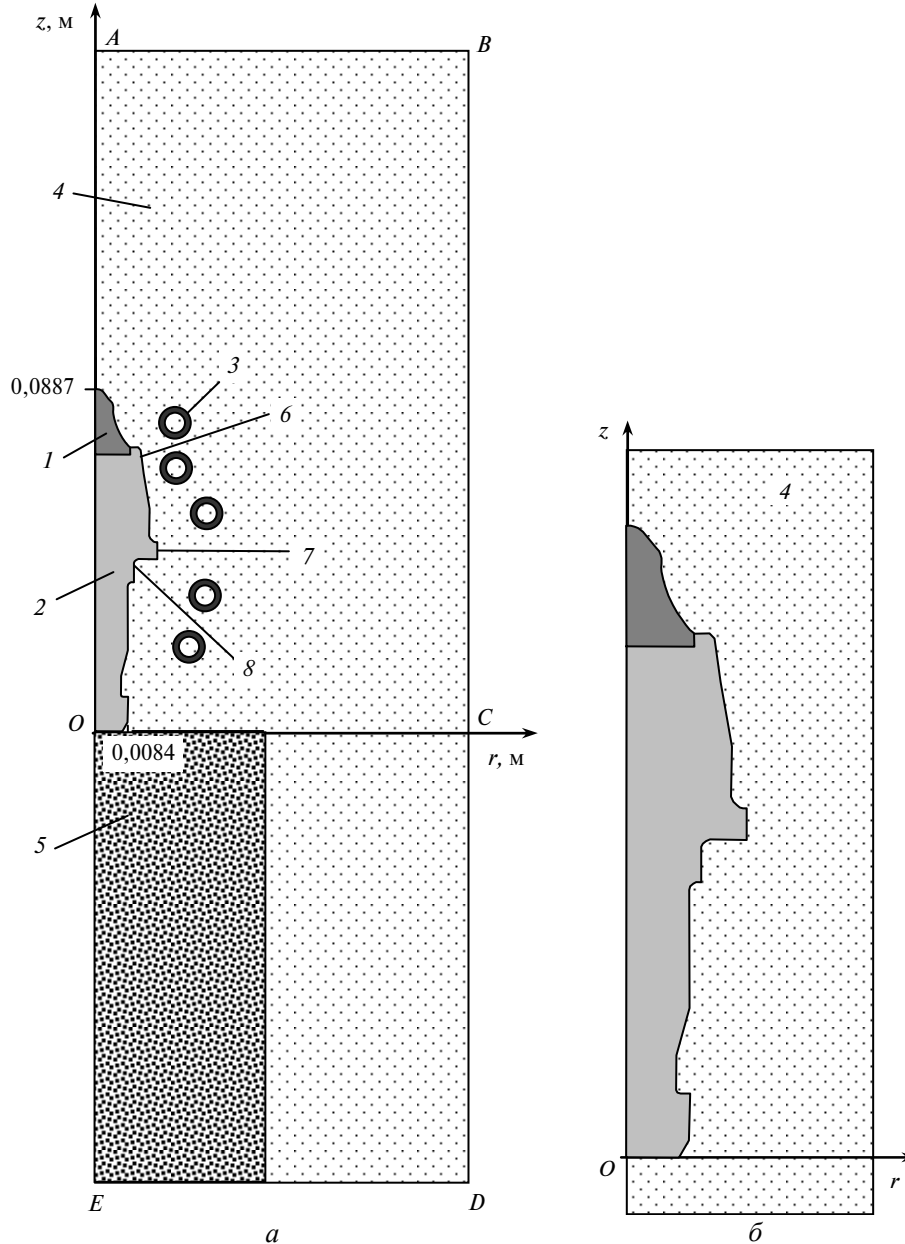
Розрахункова схема (половина осьового перерізу) індукційного паяння (а) та охолодження (б) різця на повітрі: 1 — вставка різця (твердий сплав ВК8); 2 — державка різця (сталь 35ХГСА); 3 — витки індуктора (мідь); 4 — повітряне середовище; 5 — підставка; 6 — зона поверхні різця біля вставки; 7 — буртик корпусу різця; 8 — зона поверхні різця біля буртика.
